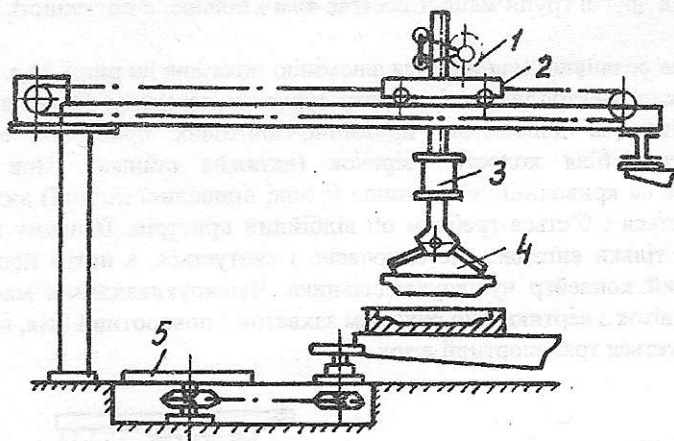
Схема машини для зйому і укладення свинцевих чушок: 1-рейкова передача; 2-вिकатний візок; 3-пневмоциліндр; 4-вилочний захват; 5-поворотний стіл
